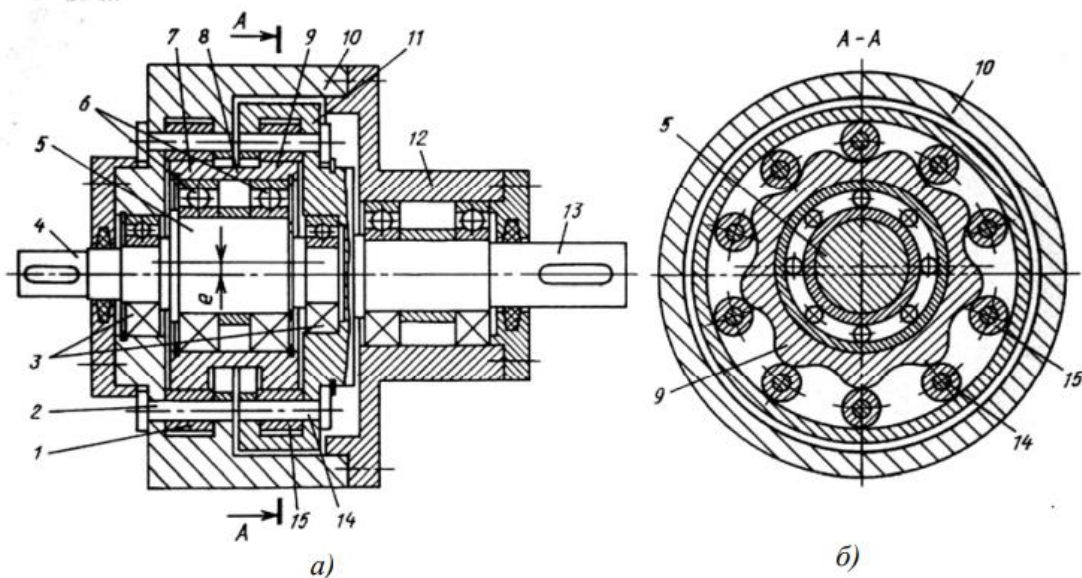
Планетарный циклоидальный редуктор с неподвижным и подвижным коронными колесами
